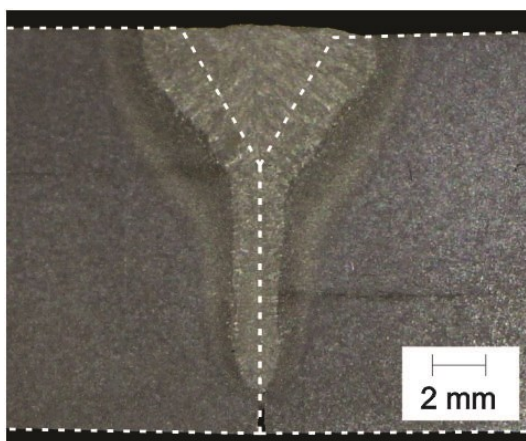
Macrografia de solda realizada pelo processo HLAW aplicado em junta com utilização de *backing* e potência Laser de 10 kW e 1m/min de velocidade de soldagem.
